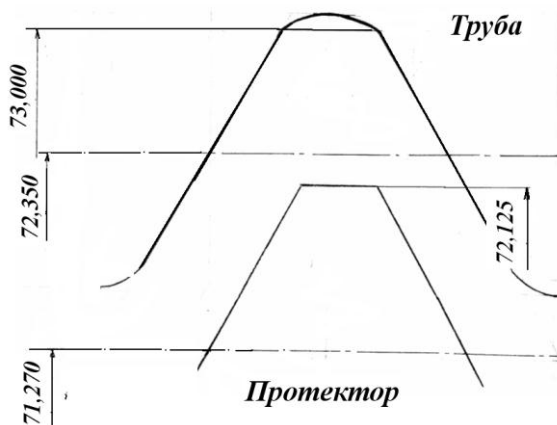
Взаиморасположение первого витка резьбы трубы и протектора
